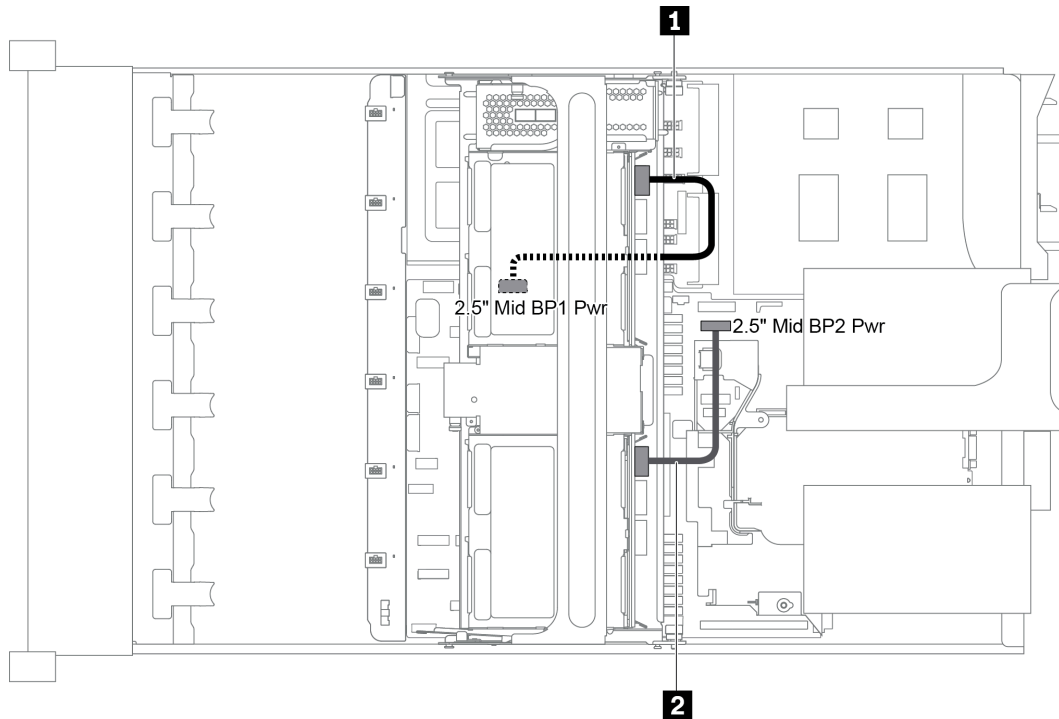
Câblage d'alimentation pour les fonds de panier d'unité centraux 2,5 pouces
